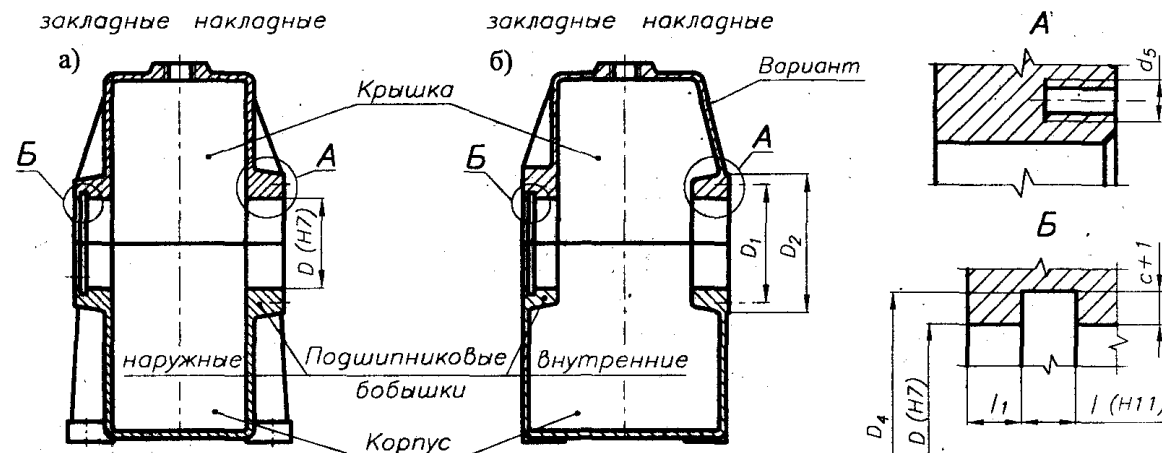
Поперечные сечения по подшипниковым узлам цилиндрического редуктора, выполненного с расположением подшипниковых бобышек: а) наружным; б) внутренним
